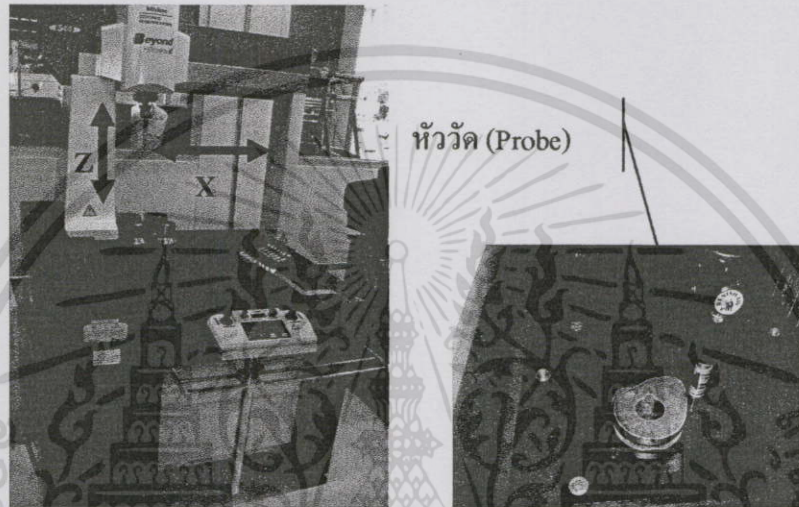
เครื่องจักร Machine Center (CNC)
